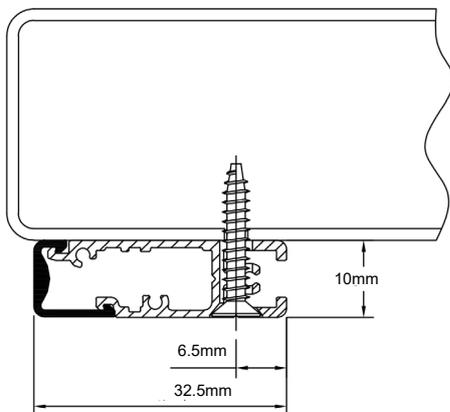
Perfil de 10 mm fijado con tornillo avellanado autorroscante
